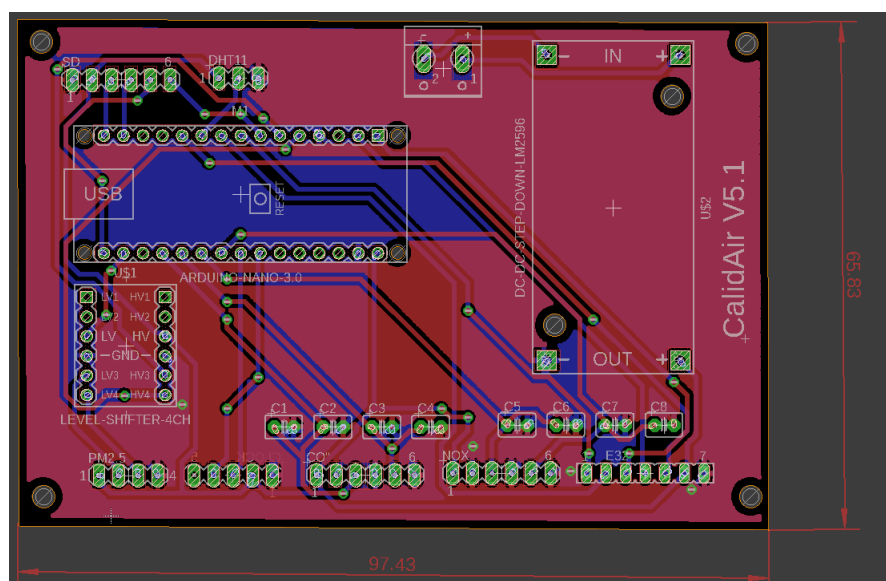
Detalles de configuración del autoroute. (Autor)
